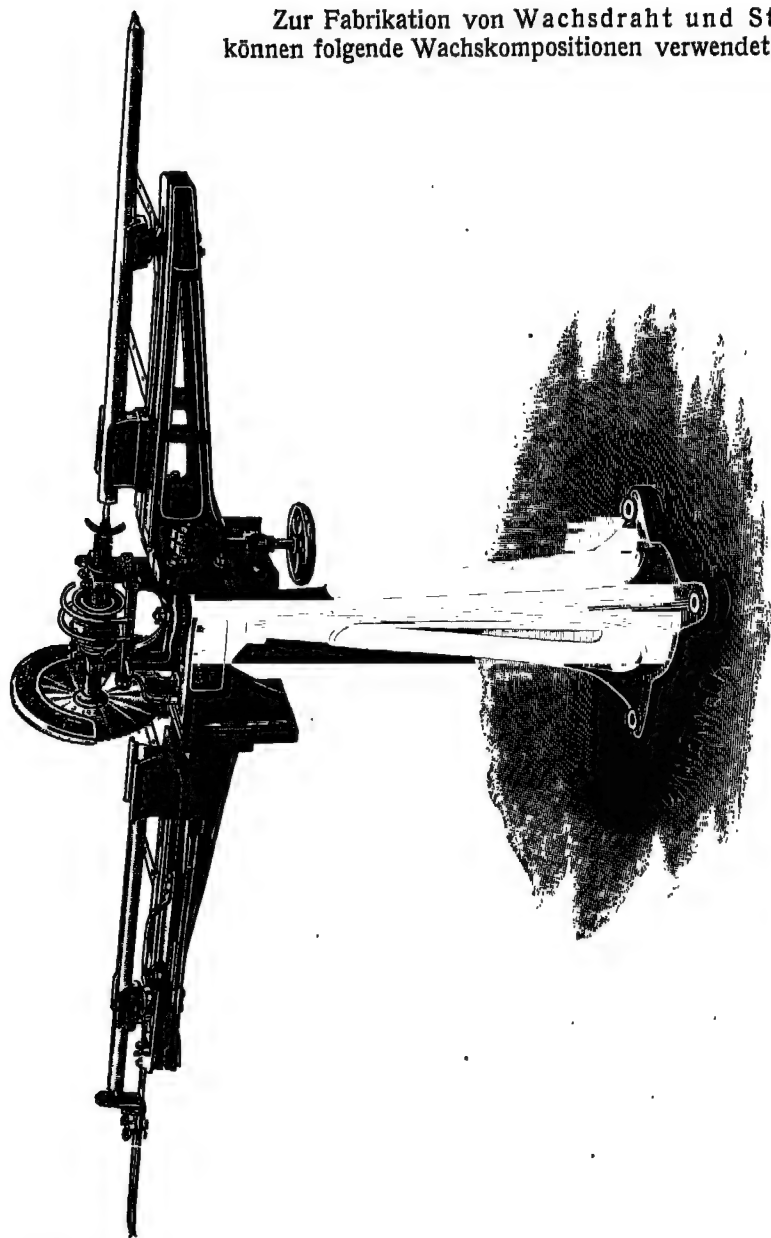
Kerzensäge, Bohr- und Fräsmaschine.
